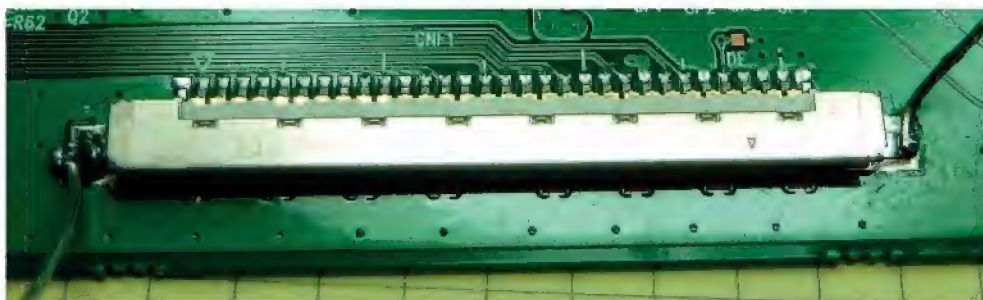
Connecteur femelle à languettes plates (connexion de signaux LVDS de téléviseur)
